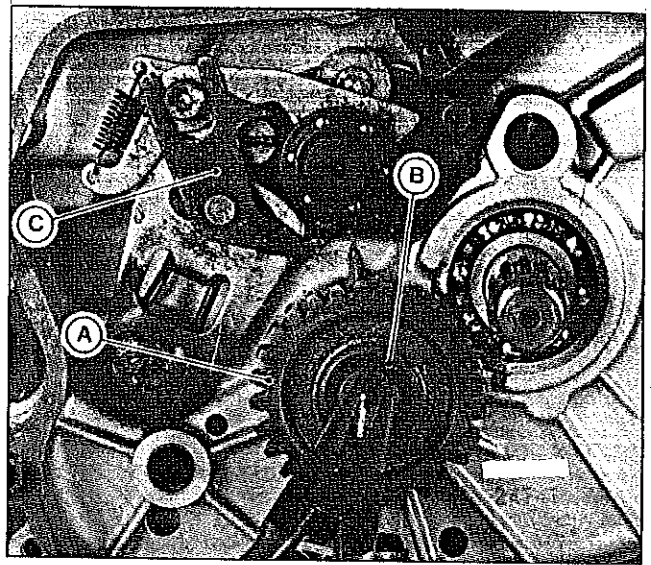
A. ENGENRAGEM INTERM. DO ARRANQUE
